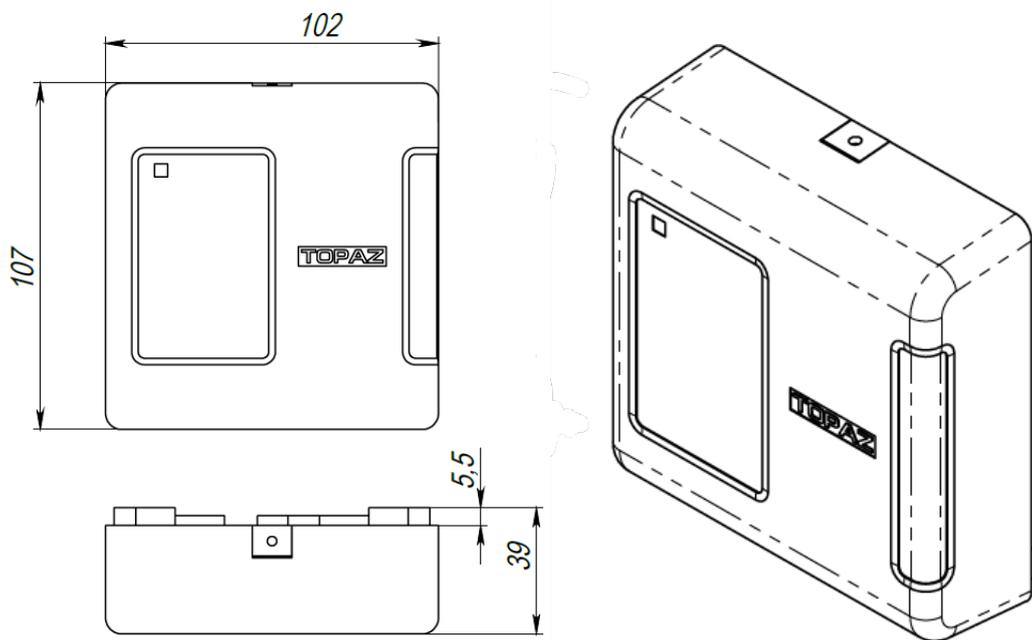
Габаритные размеры и внешний вид СП-2
